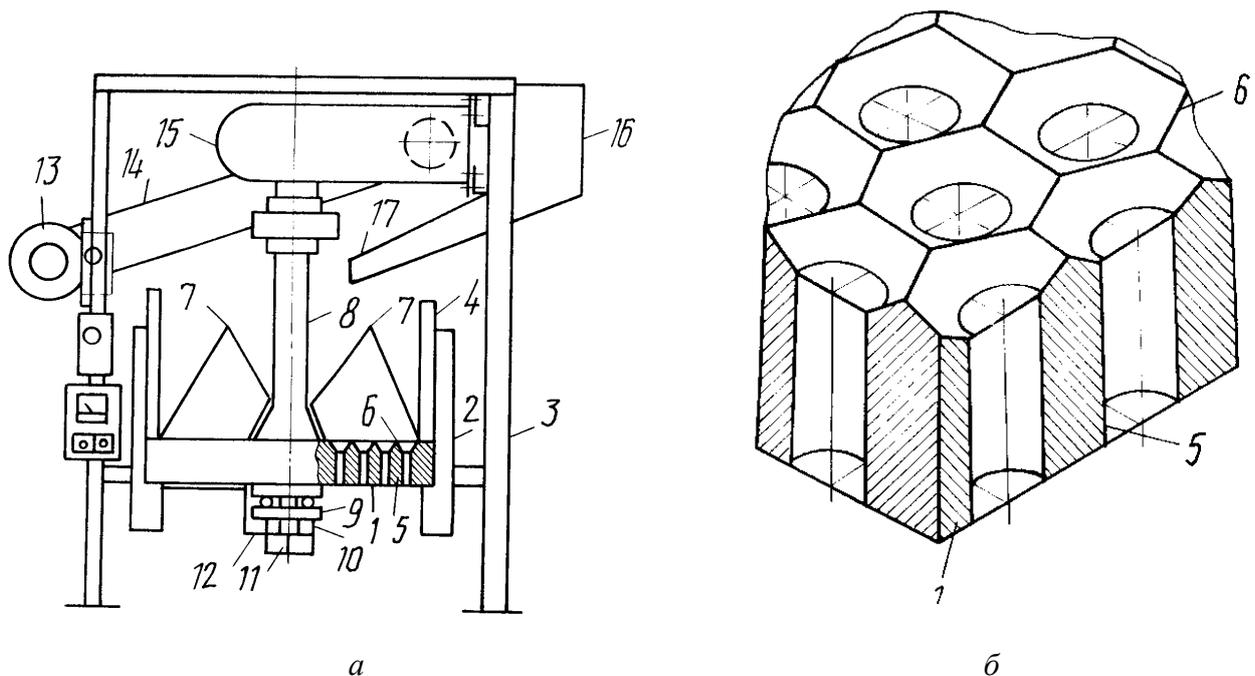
Пресс-гранулятор: 1 – матрица; 2 – обойма; 3 – рама; 4 – кольцо; 5 – прямые режущие кромки; 6 – ячейки; 7 – конические вальцы; 8 – приводной вал; 9 – упорный подшипник; 10, 12 – гайка; 11 – подрезной нож; 13 – электродвигатель; 14 – клиноременная передача; 15 – редуктор; 16 – бункер; 17 – задвижка
